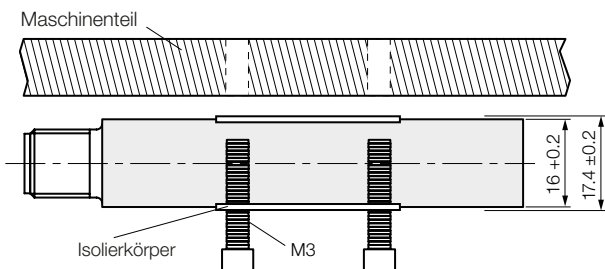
Sensorkopf mit Isolierkörper montieren
